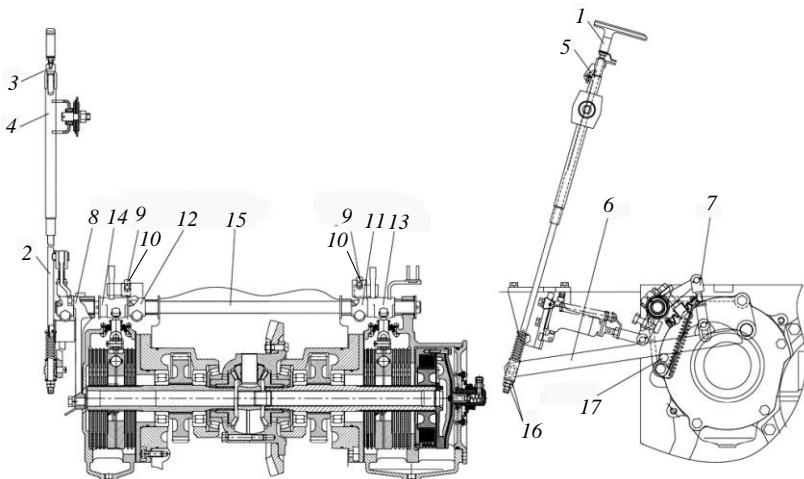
Регулировка привода стояночного тормоза: 1 – рукоятка; 2, 7 – тяги; 3 – штифт; 4, 8 – кронштейны; 5 – фиксатор; 6 – рычаг; 9 – контргайка; 10 – болт регулировочный; 11, 13 – рычаги правого тормоза; 12, 14 – рычаги левого тормоза; 15 – валик; 16 – гайки; 17 – болт-оправка
